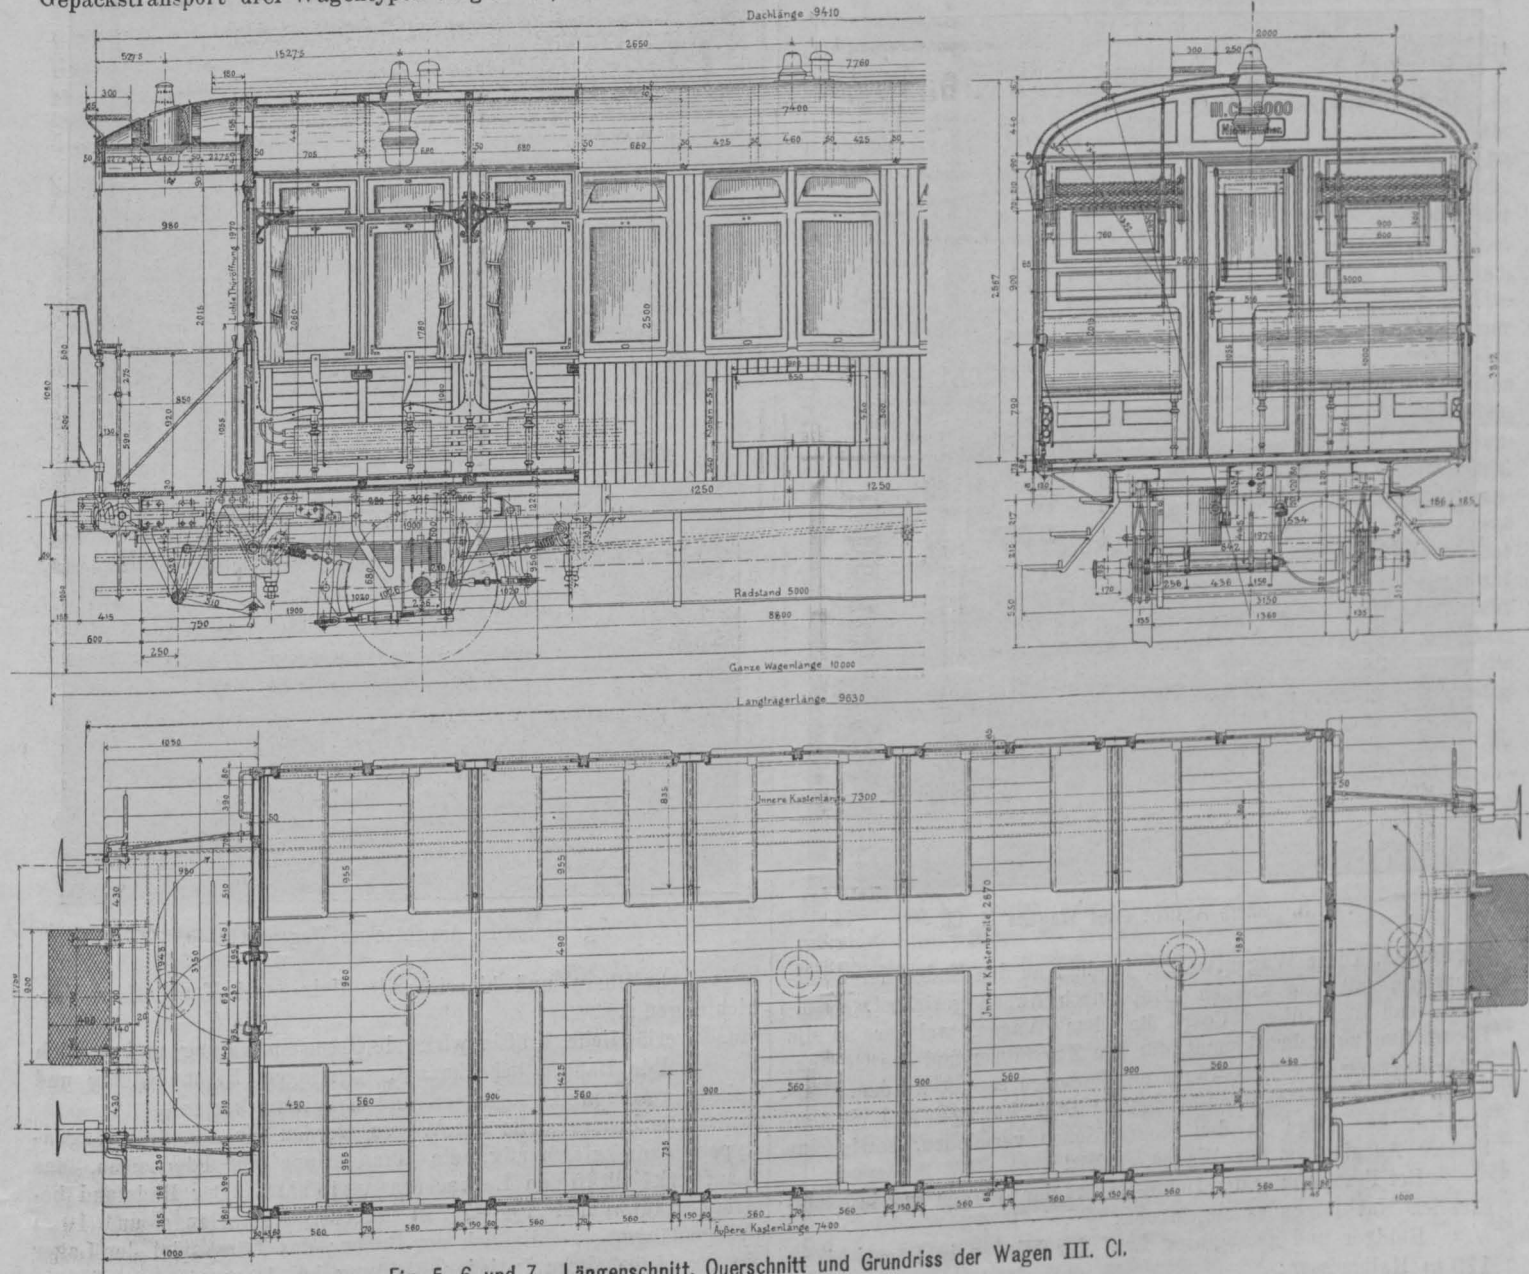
, 6 und 7. Längenschnitt, Querschnitt und Grundriss der Wagen III. Cl.
